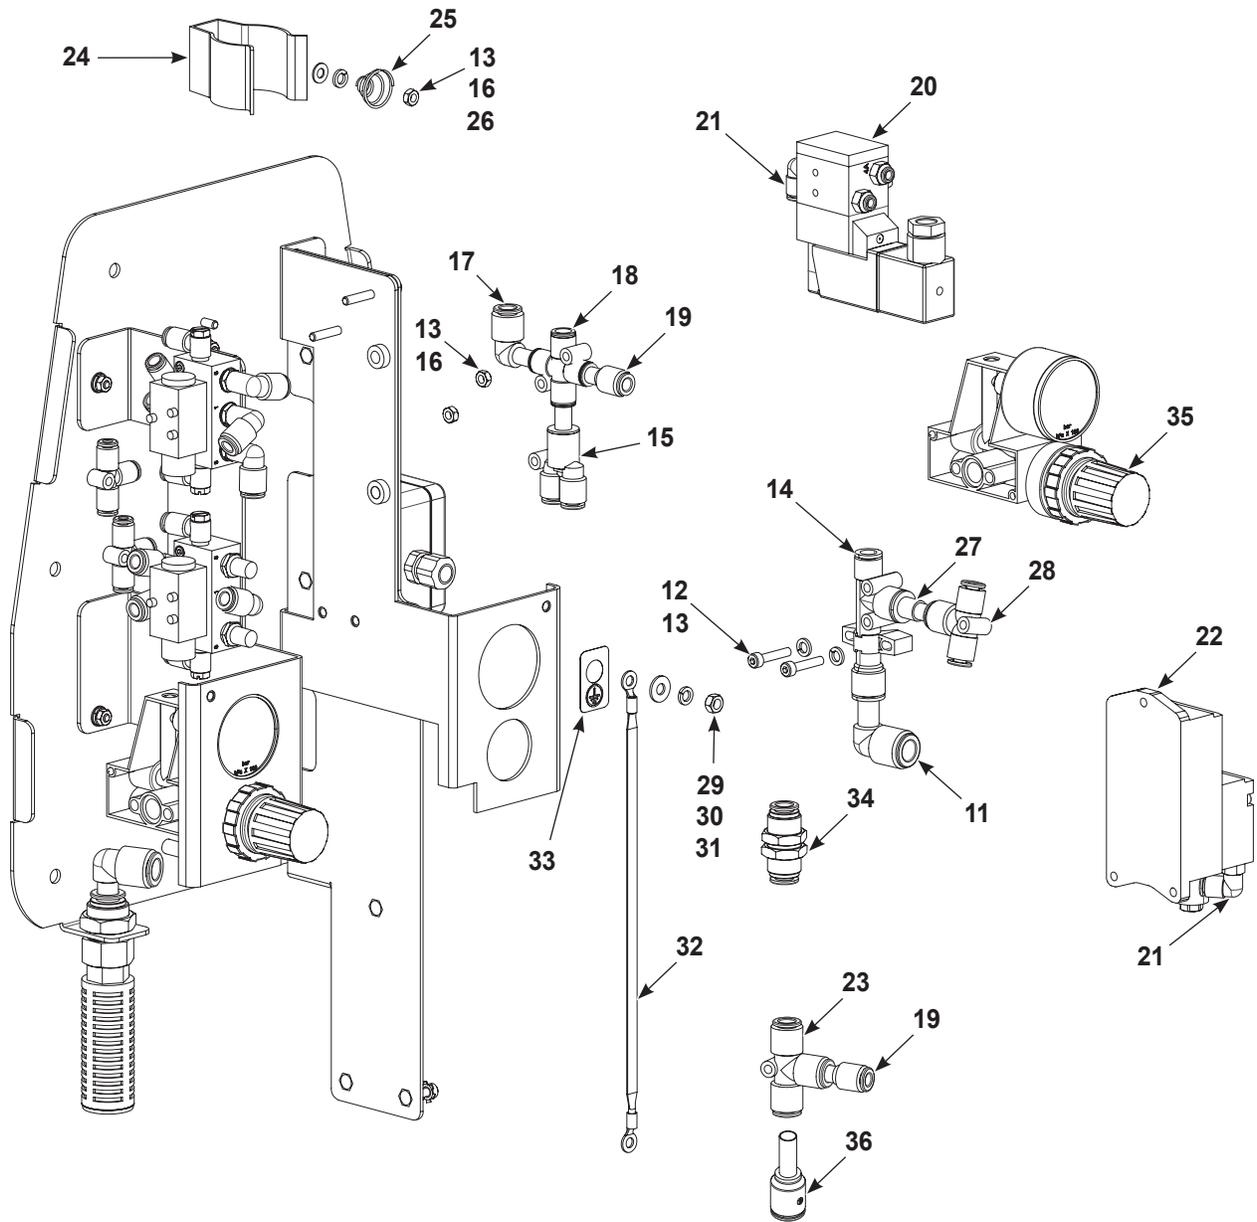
Pumpensteurelemente – rechte Seite (Abbildung für Version mit Generator)
